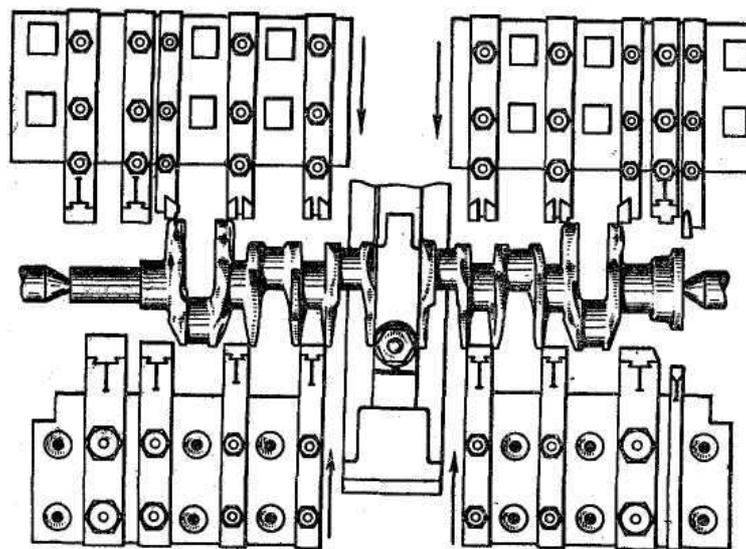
Схема обтачивания коренных шеек и концов коленчатого вала на токарном полуавтомате с центральным приводом
